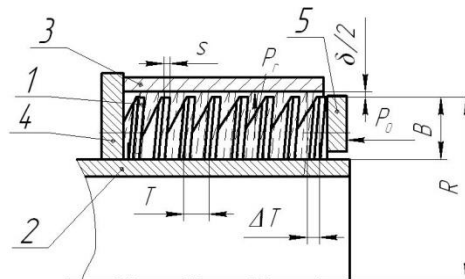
Розрахункова схема геометричних параметрів затиску заготовки гвинтовим затискним елементом з конічними частинами: 1 – гвинтовий затискний елемент, 2 – корпус оправки, 3 – заготовка, 4 – упорне кільце, 5 – затискна втулка
